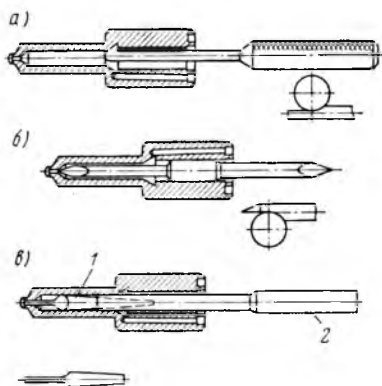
Скребки для очистки внутренних полостей корпуса распылителя форсунки:
